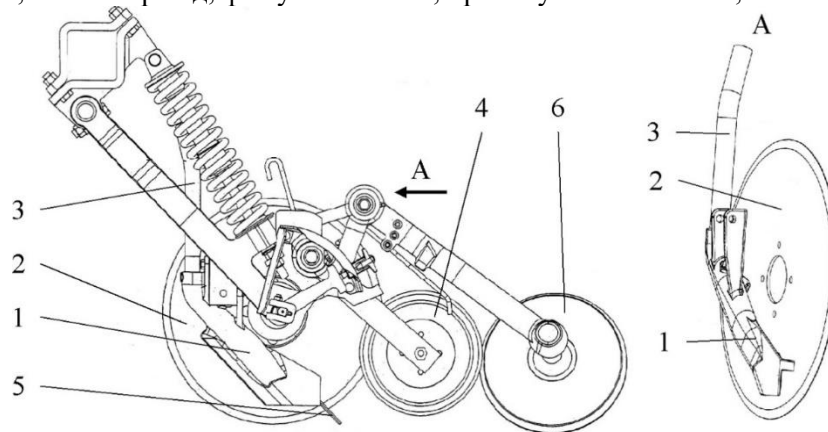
Конструктивно-технологічна схема висівної секції пневматичної сівалки точного висіву John Deere 90 Series [5]: 1 – висівний башмак (Seed Boot); 2 – однодисковий сошник (Single Disc Furrow Opener); 3 – насіннепровід (Seed Tube); 4 – фіксує колесо (Seedlock Wheel); 5 – заспокоювач насіння (Seed Flap); 6 – прикочувальне колесо (Closing Wheel)
